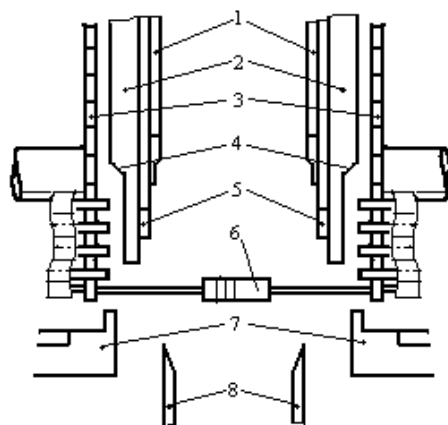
Установочная головка для ЭРЭ с осевыми выводами
